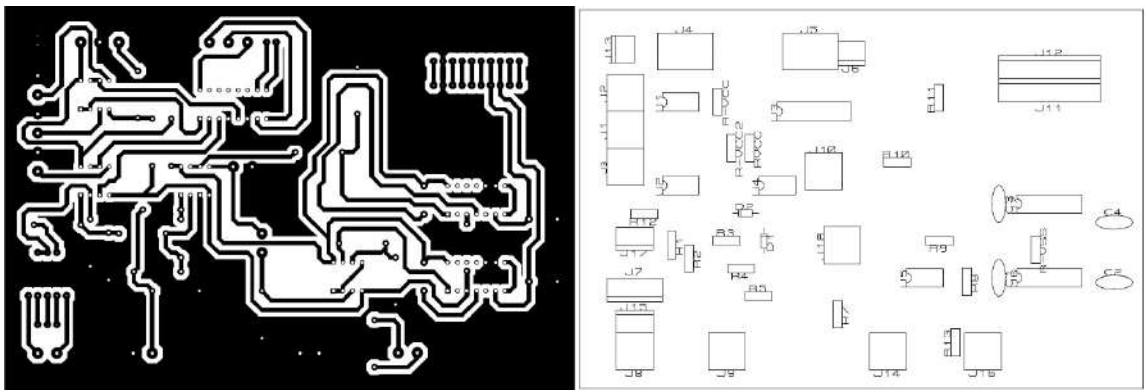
Diseño de las pistas de la PCB y acotaciones.
